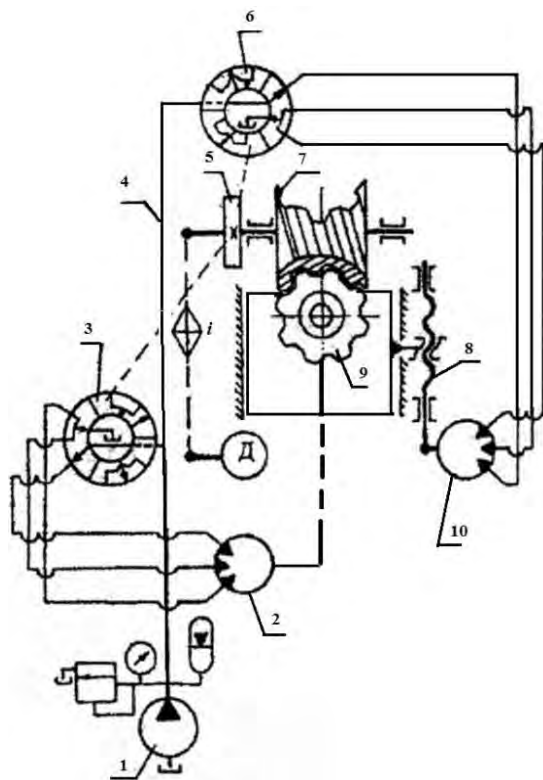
Структурная схема резьбонарезного станка с гидравлическими связями для нарезания глобоидных червяков
